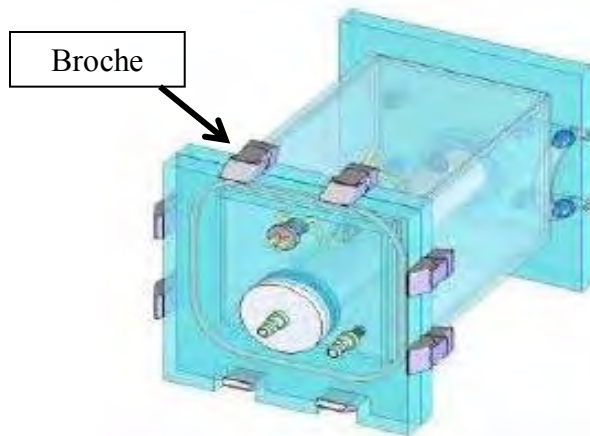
Diseño en CAD del tanque, año 2006 [21].
